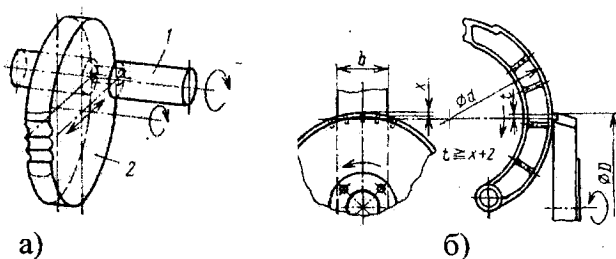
Схеми фрезерування циліндричної поверхні:
